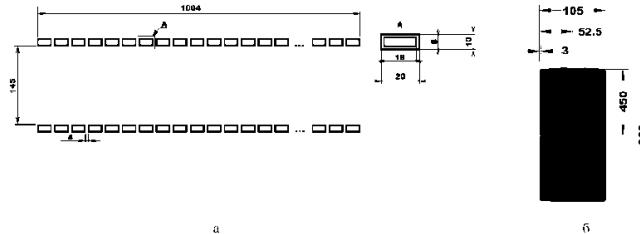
Геометрические размеры периодической индукционной установки (а) и нагреваемой заготовки (б)
